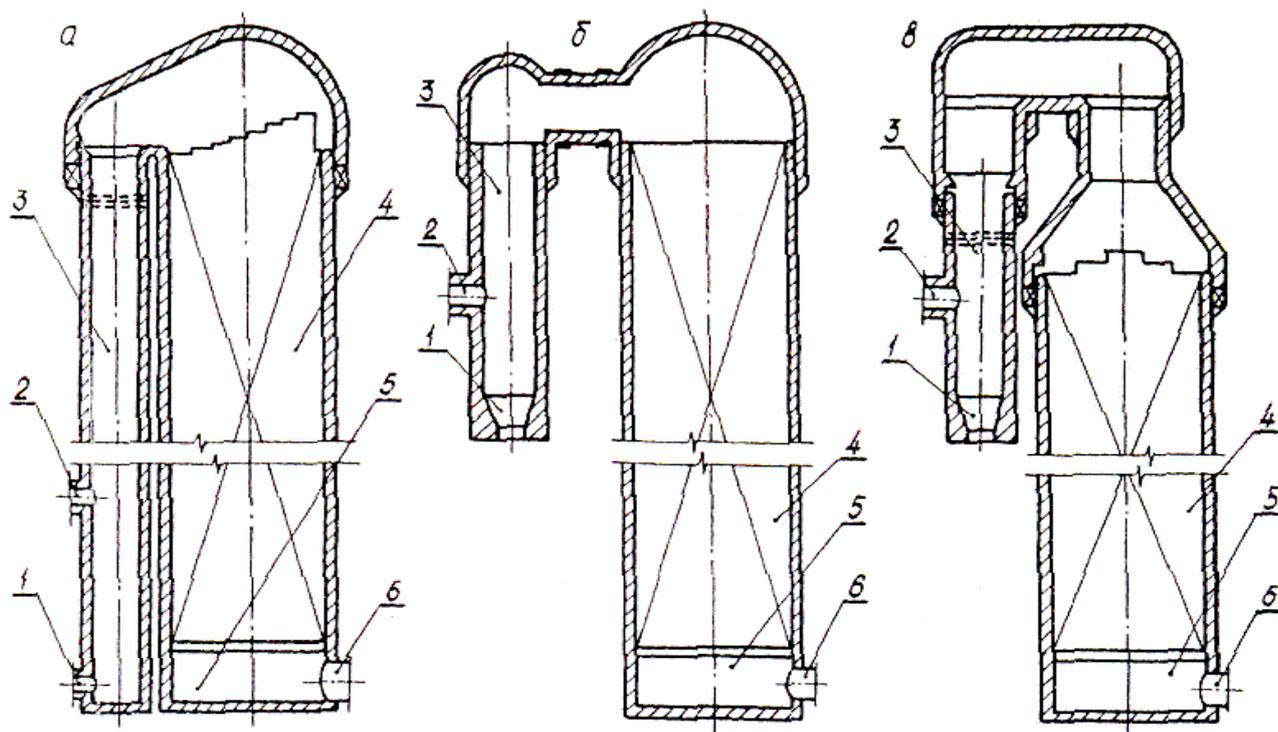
Варианты воздухонагревателя с выносной камерой горения: а – конструкция Дидье; б – Коппера и в – Мартина-Пагенштехера: 1 – штуцер горелки; 2 – штуцер горячего дутья; 3 – камера горения; 4 – насадка; 5 – поднасадочное устройство; 6 – дымовой патрубок
